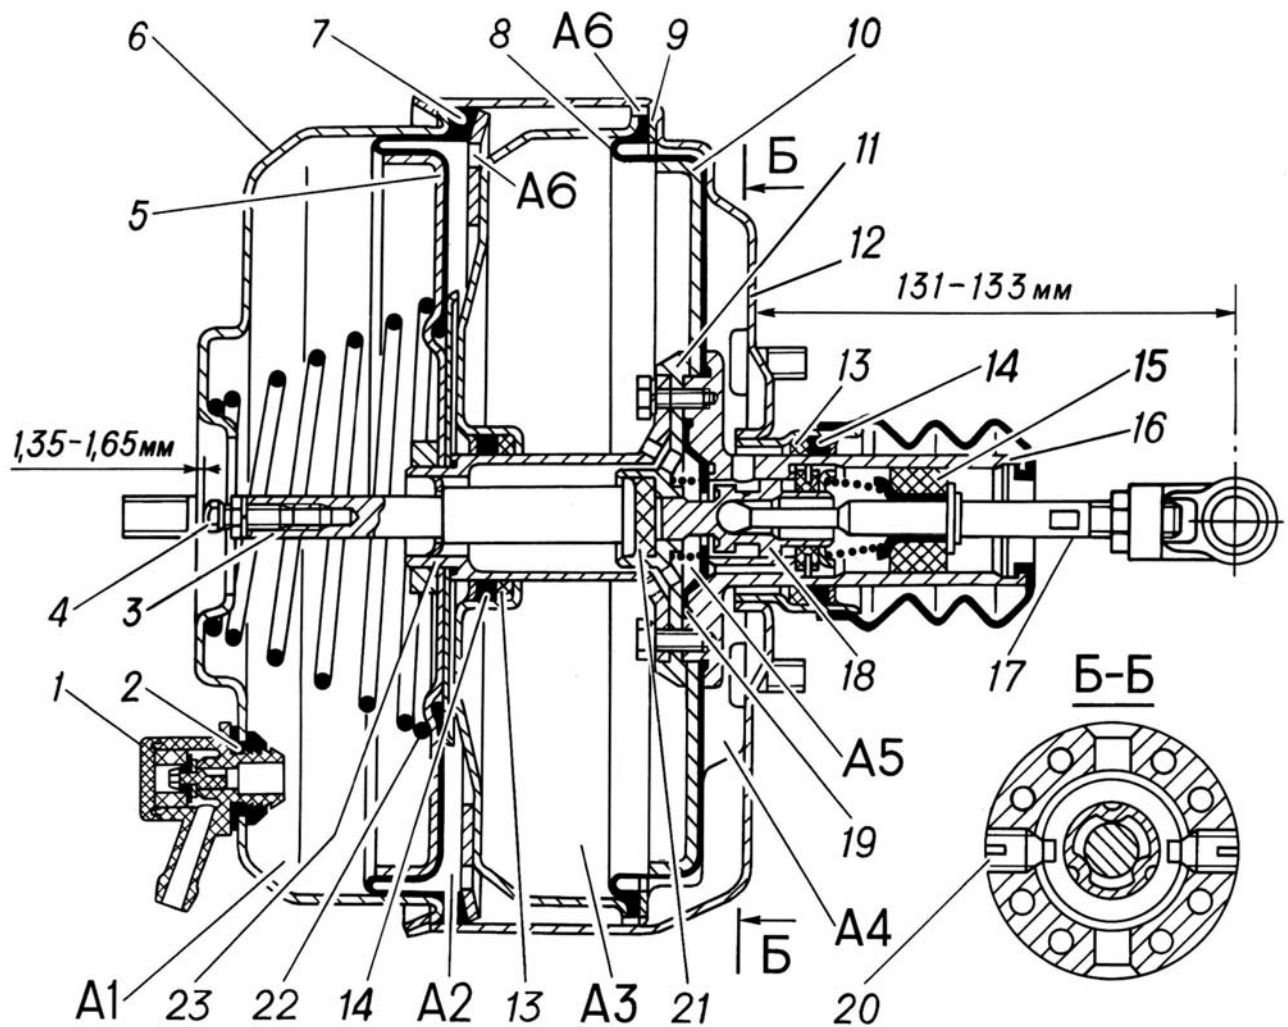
Вакуумный усилитель: А1, А2, А3, А4 и А5 - полости вакуумного усилителя; А6 - отверстия; 1 - обратный клапан; 2 - уплотнительная втулка; 3 и 17 - толкатели; 4 - регулировочный болт; 5, 10 и 18 - поршни; 6 - крышка; 7 и 8 - диафрагмы; 9 - упорное кольцо; 11 - фланец поршня; 12 - корпус усилителя; 13 - направляющие кольца; 14 - уплотнительные манжеты; 15 - фильтр; 16 - корпус клапанов; 19 - диафрагма клапанов; 20 - винт; 21 - реактивная шайба; 22 - пружина; 23 - соединитель поршней
